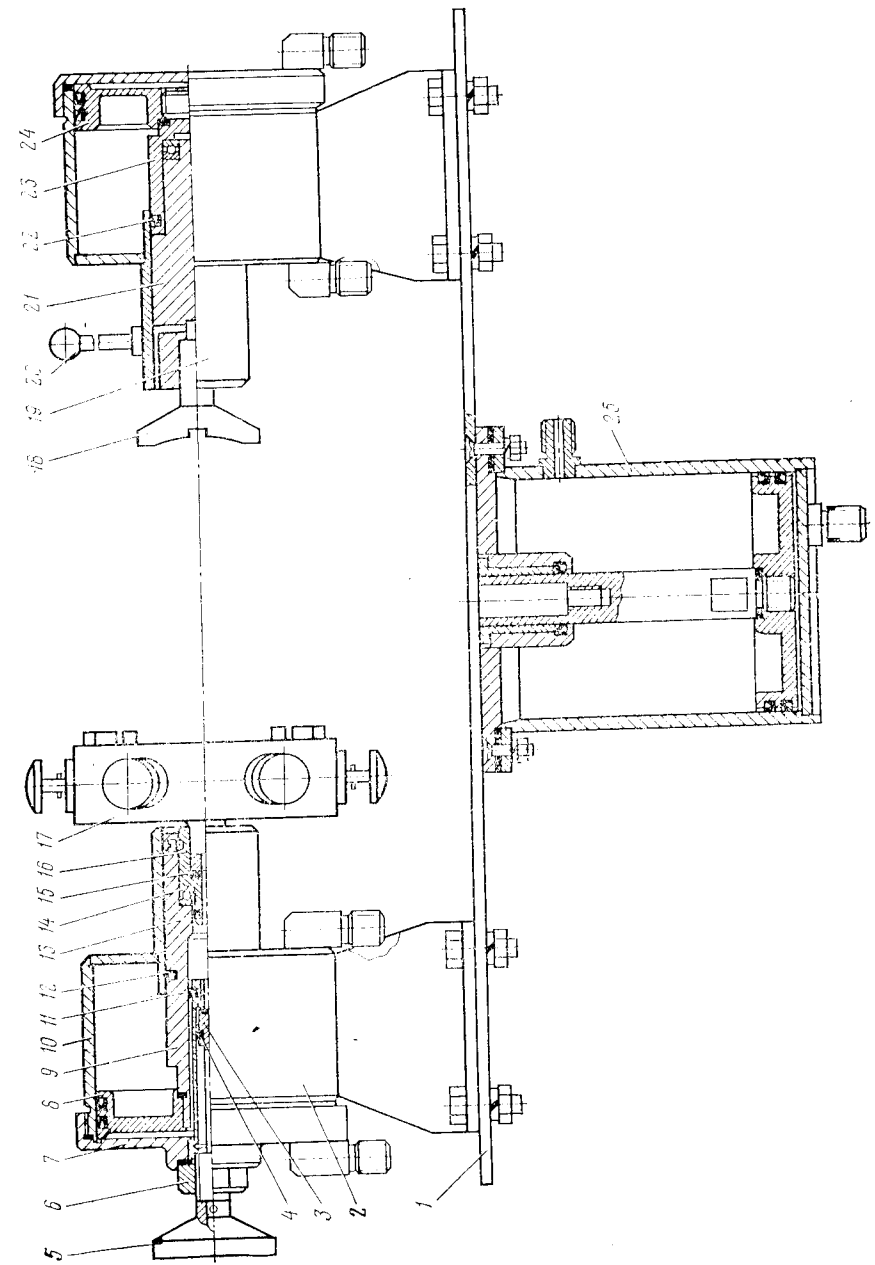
Приспособление для разборки, сборки и испытания тормозных приборов
